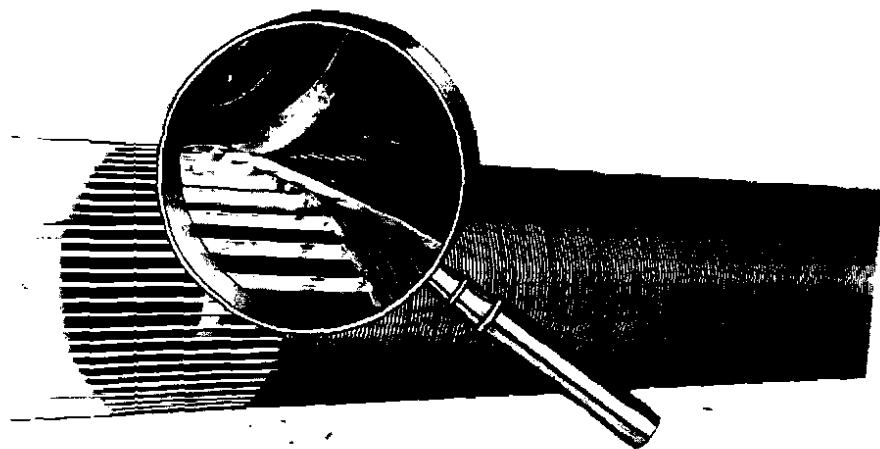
Fabricación de la rejilla Johnson de ranura continua y soldadura global, para pozos de agua y de petróleo. La rejilla puede fabricarse de cualquier metal o aleación que sea resistente a la soldadura.
